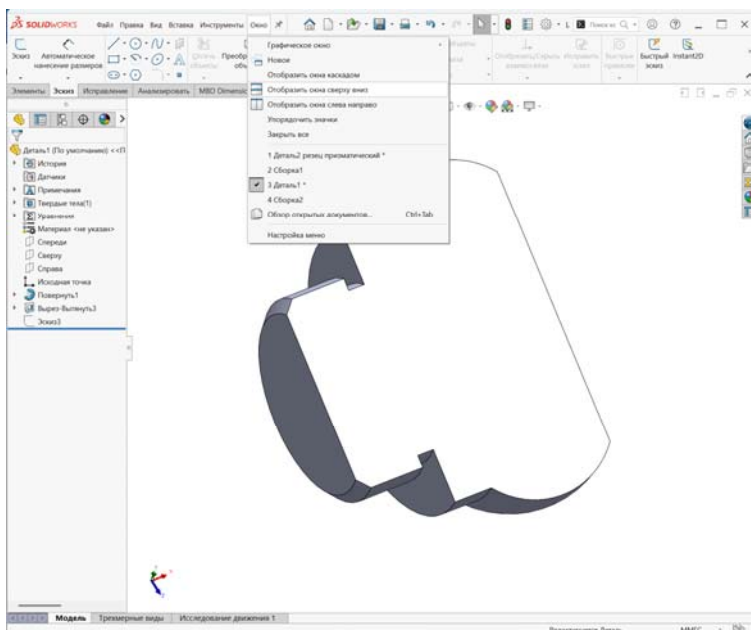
Вставка твердотельной модели детали и твердотельной модели призматического фасонного резца в сборку
